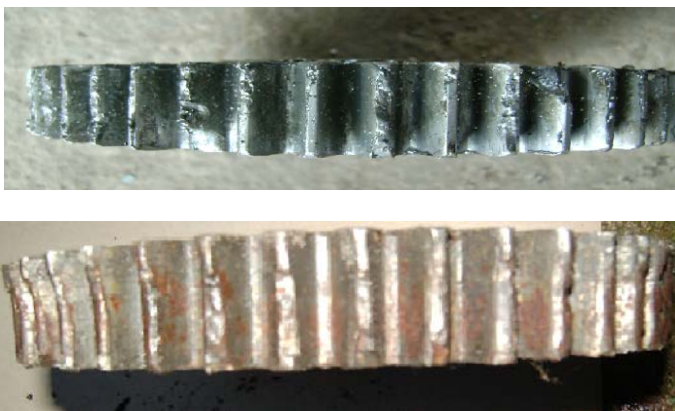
Шестерни режущего аппарата с изношенными зубьями
